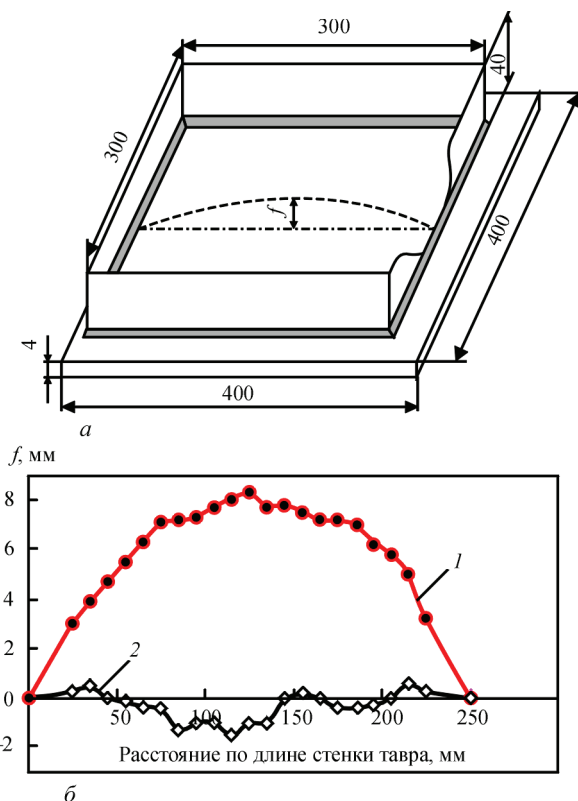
Образец сварного соединения из сплава АМгб с бухтиной: а — схема образца (f — прогиб); б — формоизменения образца (кривая 1 — исходные прогибы f по центру образца; 2 — f после ЭДО)
